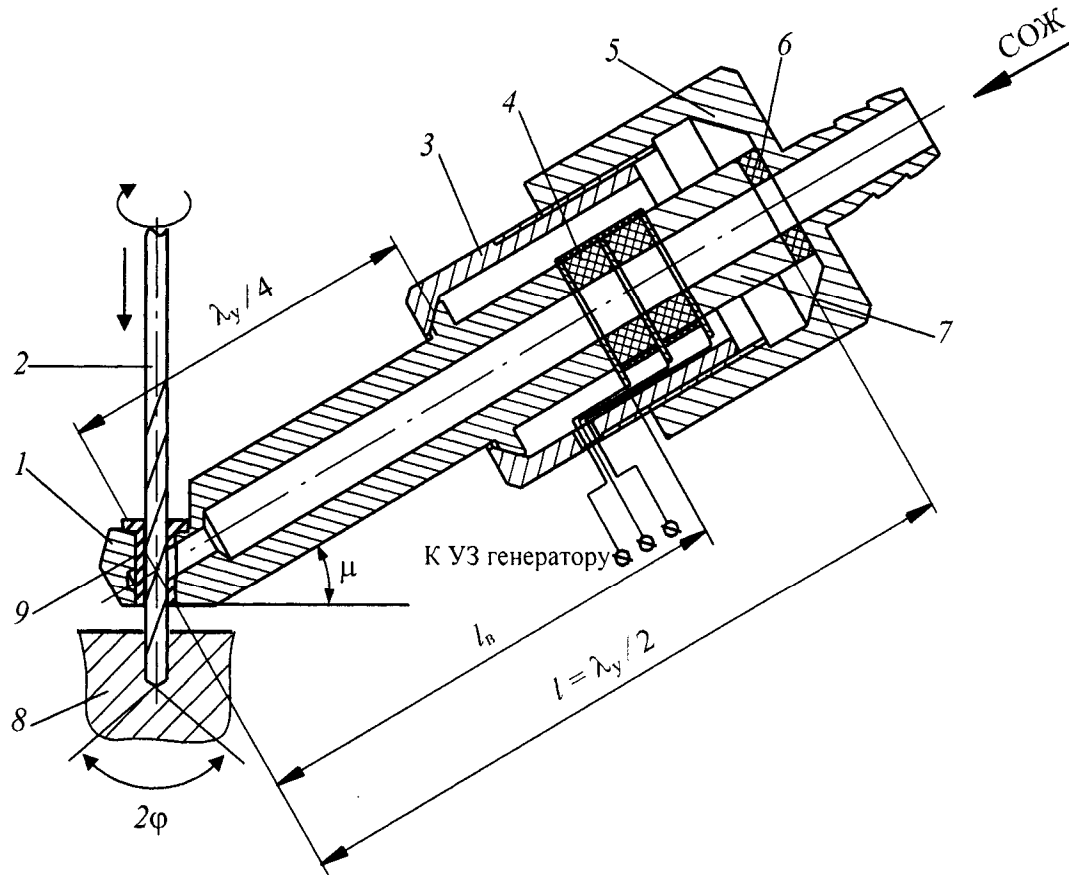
Устройство для наложения УЗК на СОЖ и сверло: 1 - волновод; 2 - сверло; 3 - стакан; 4 - пьезопреобразователь; 5 - штуцер; 6 - прокладка; 7 - отражающая шайба; 8 - заготовка
